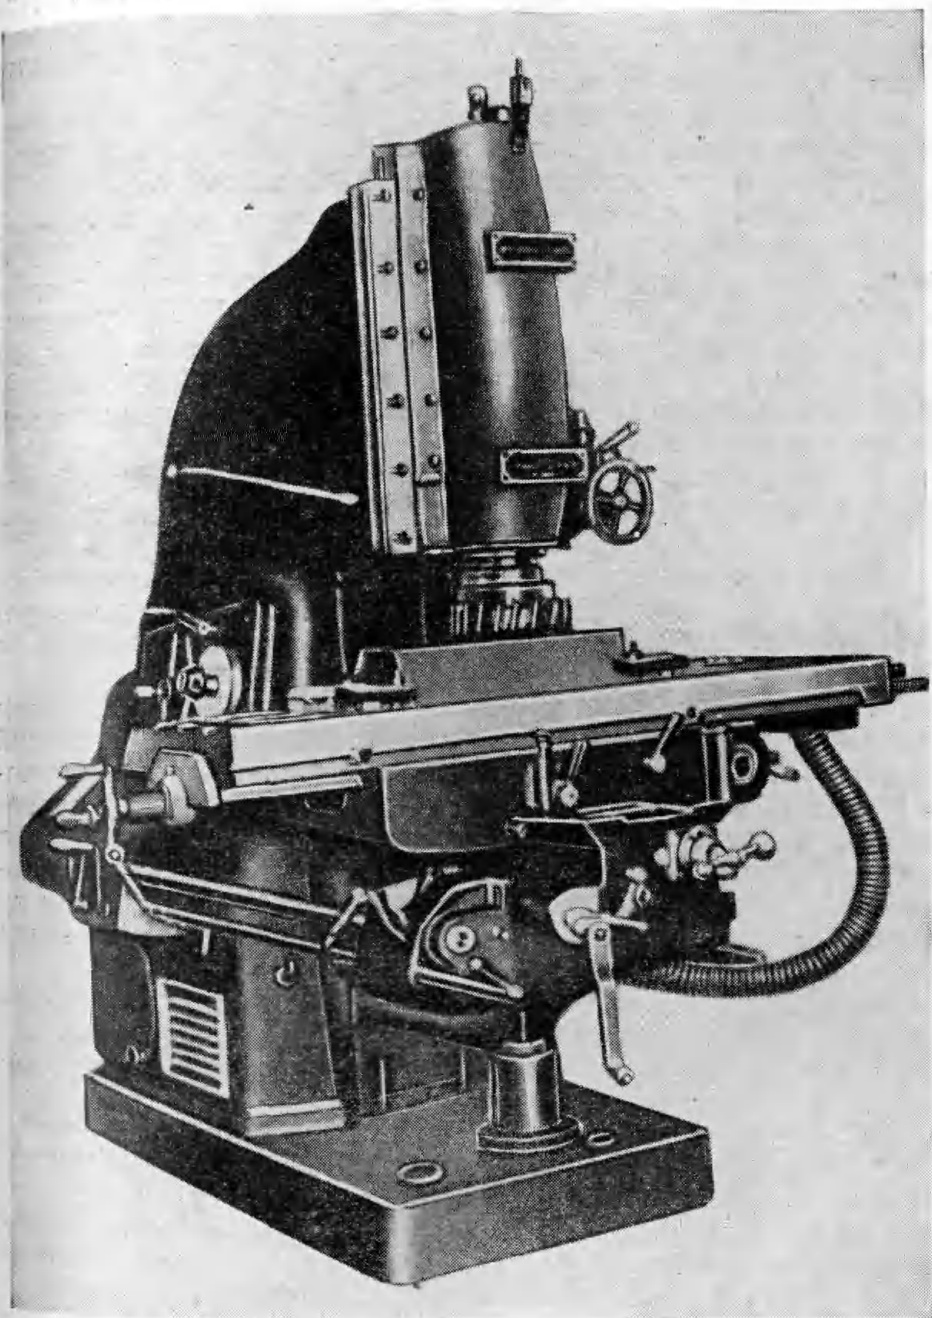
Вертикально-фрезерный станок мод. 610.
